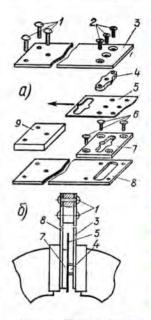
Штомп для вырубки монтожных лепестков: и — устройство, б —
